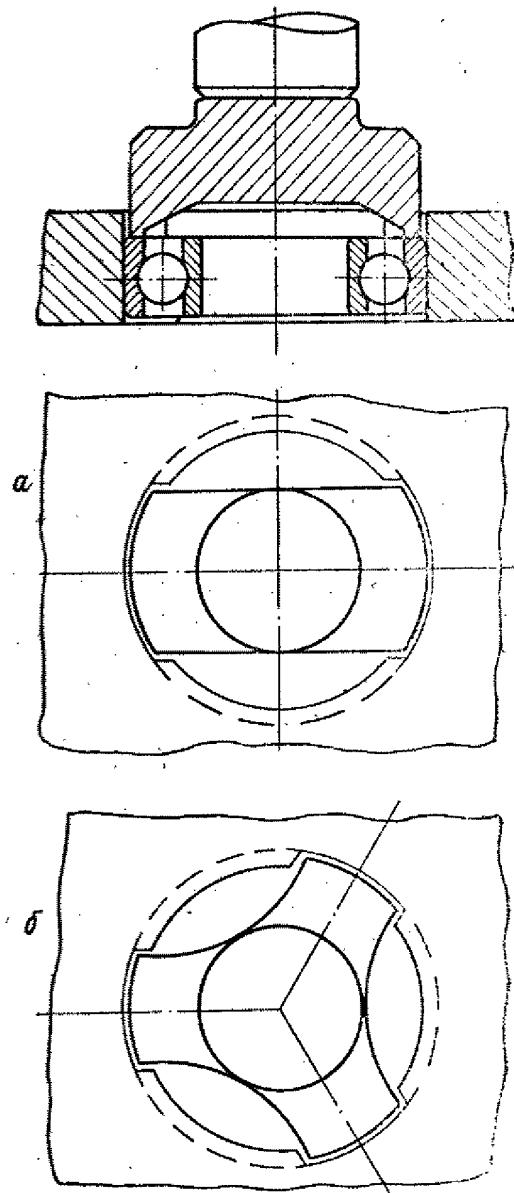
Схема демонтажа подшипника не-разборного типа из корпуса с помощью съемника с двумя (а) и с тремя (б) упорными поверхностями
